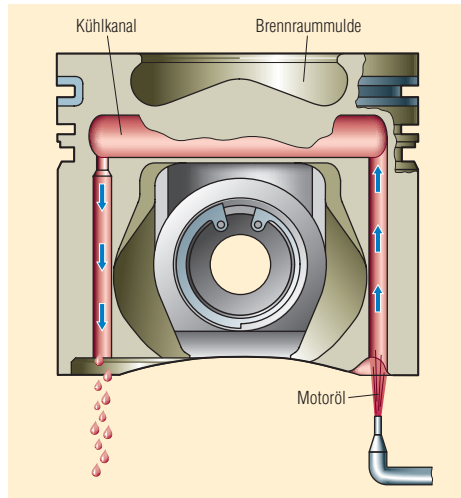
Von unten mit Öl gekühlter Kolben.
